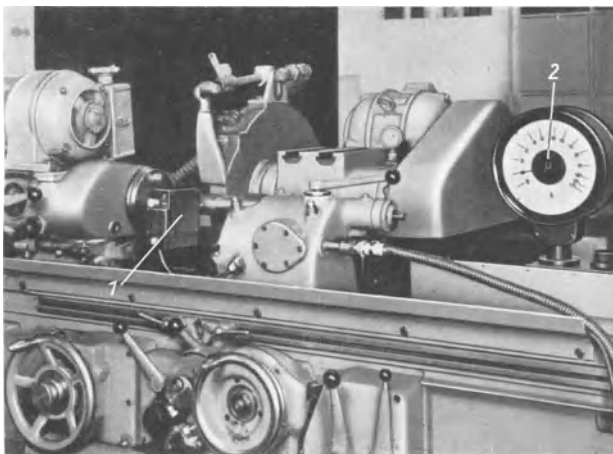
Mikrotaster an einer Schleifmaschine. 1 Bolometrischer Mikrotaster; 2 Anzeigement.
